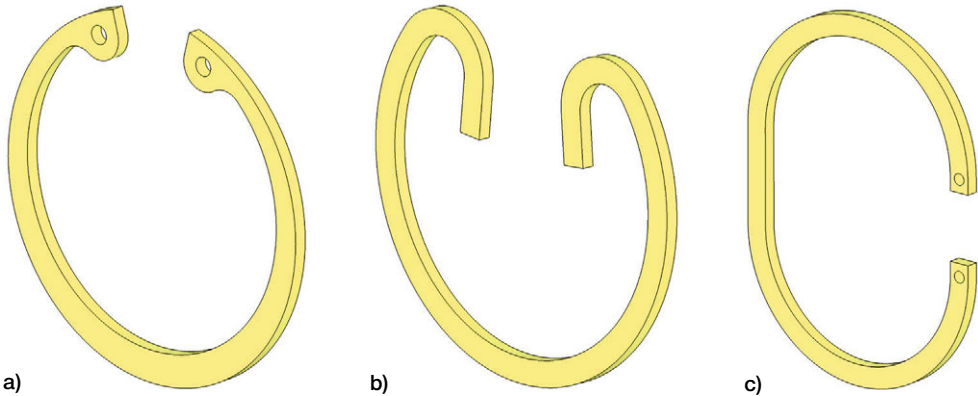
Sicherungsringe für große Kolbenbolzen:
